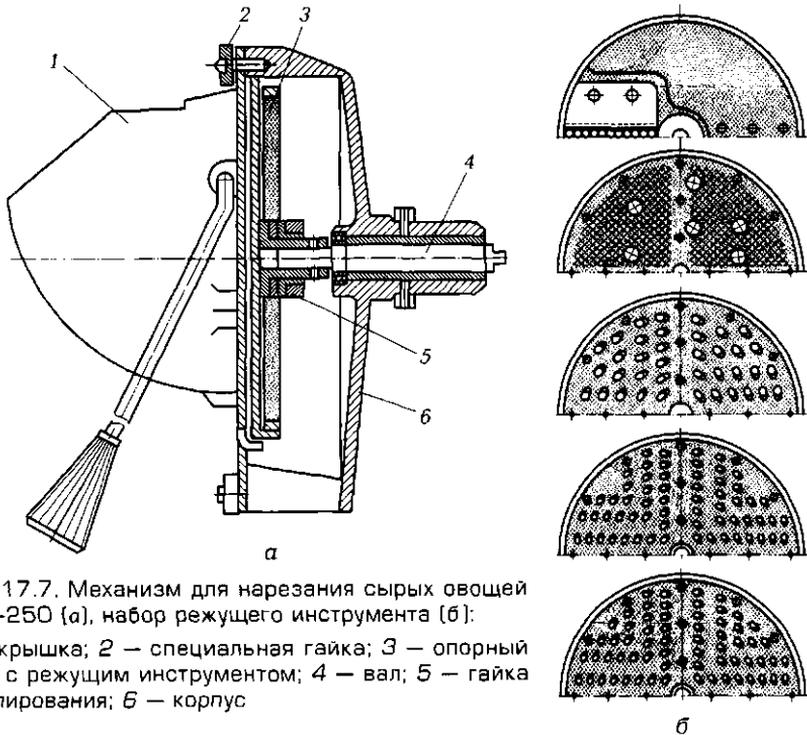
Механизм для нарезания сырых овощей МКУ-250 (а), набор режущего инструмента (б):
